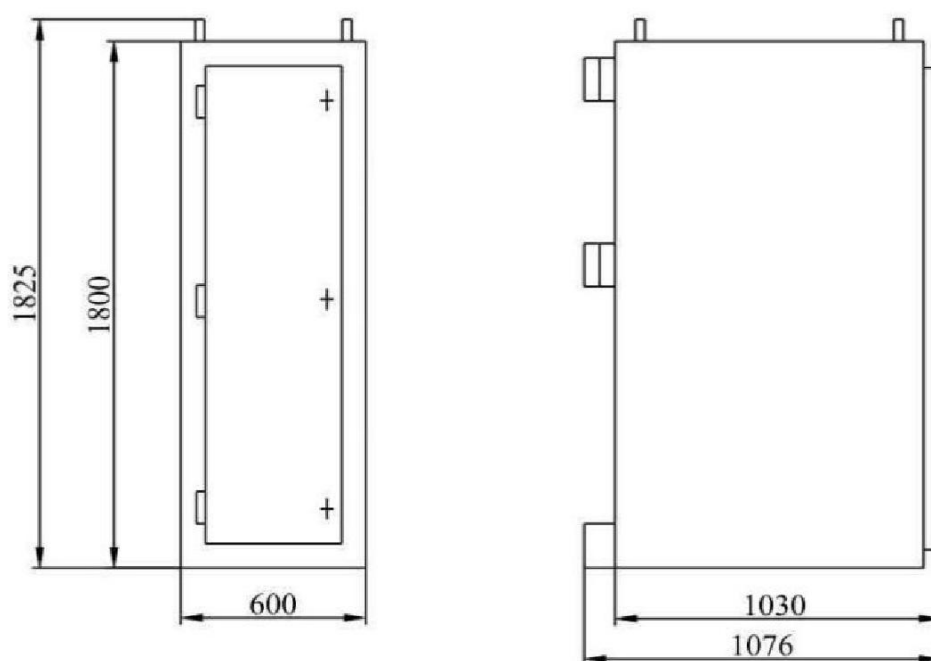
Габаритные размеры шкафов КРУ исполнения ШКА
